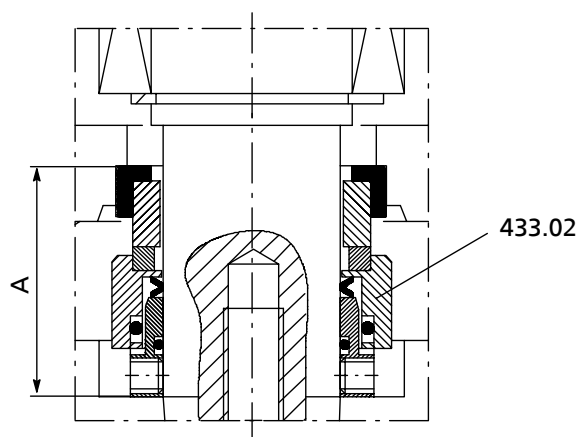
Монтажная схема торцового уплотнения с закрытыми пружинами - (HJ)
